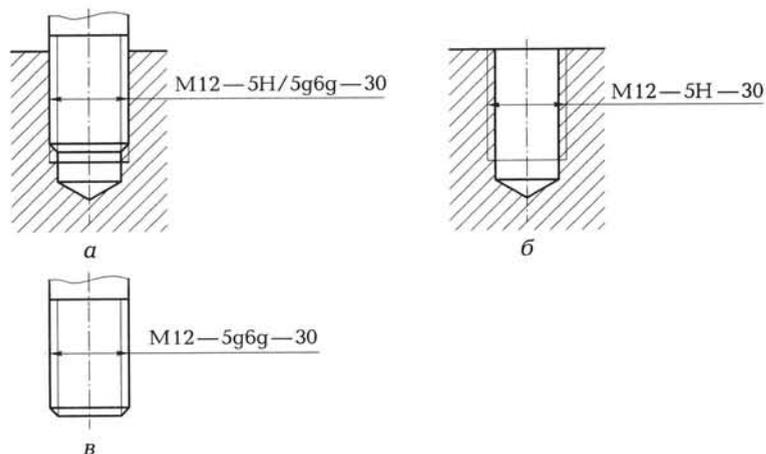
Обозначения посадки (а) и полей допусков деталей резьбового соединения для внутренней резьбы (б) и наружной резьбы (в)
